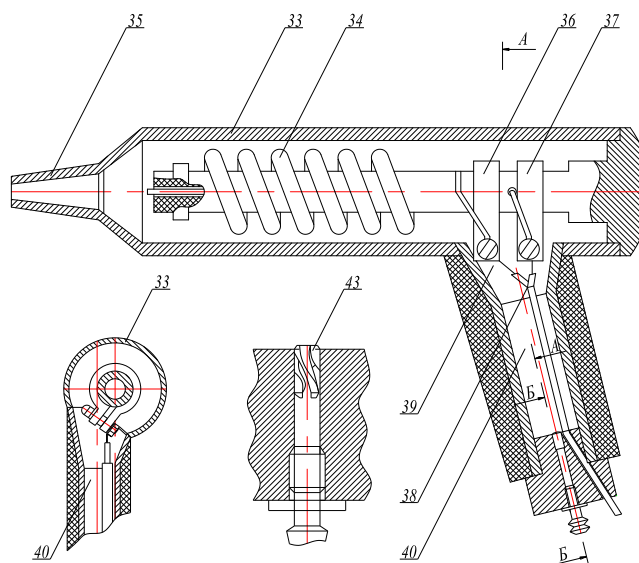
Пристрій для зварювання термопластів газоподібним теплоносієм
